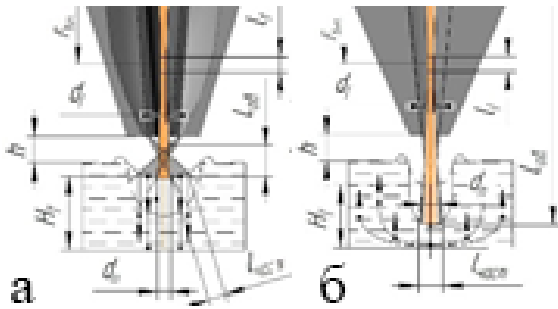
Схеми розташування фокуса лазерного випромінювання щодо перетяжки газопорошкового потоку для фурми з обробкою частинок: а – на виході, б – починаючи з середини фурми.
